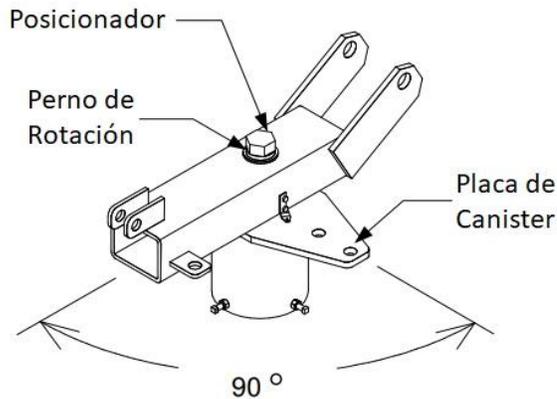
Perno de rotación del posicionador(Fuente: Material de Visión Mundial, año 2009)
